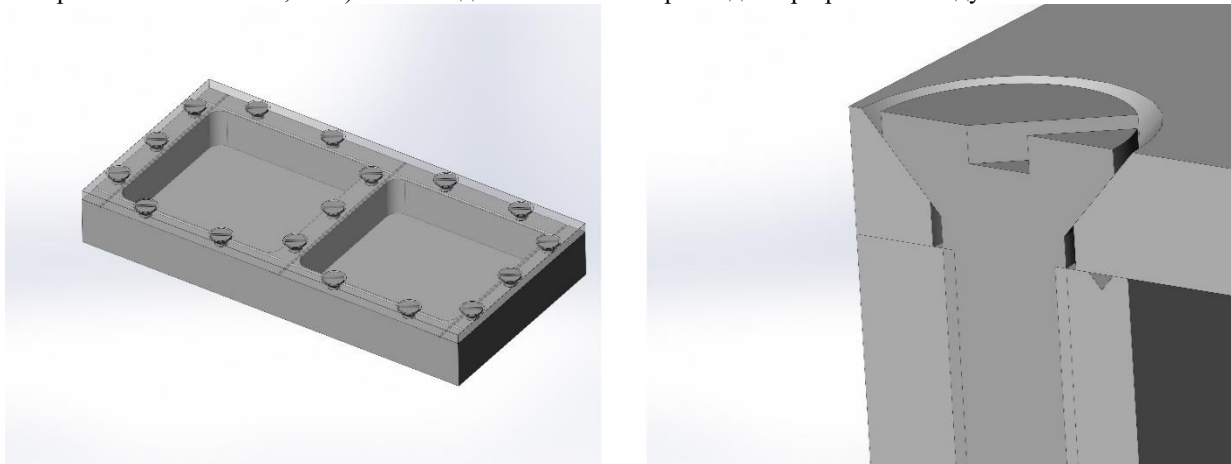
Установка крышки с уплотнением индиевой прокладкой.
